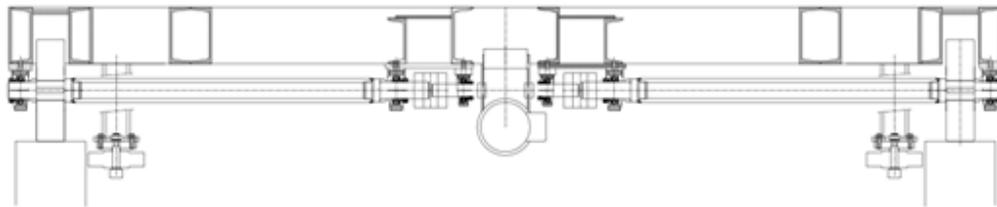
Plano 4. Detalle soporte de ruedas y placa de amarre
